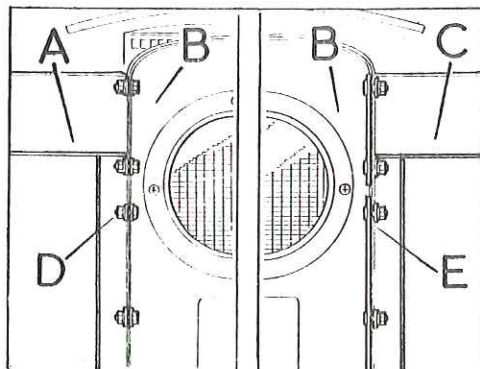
Elementos de fijación de la calandra a las aletas
